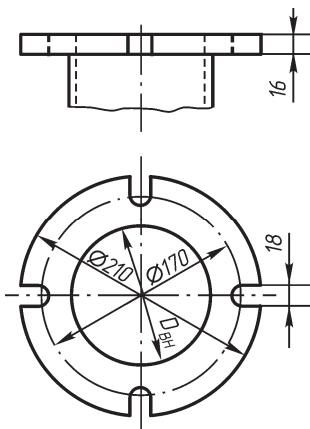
Стандартное фланцевое соединение международного образца для бытовых стоков
